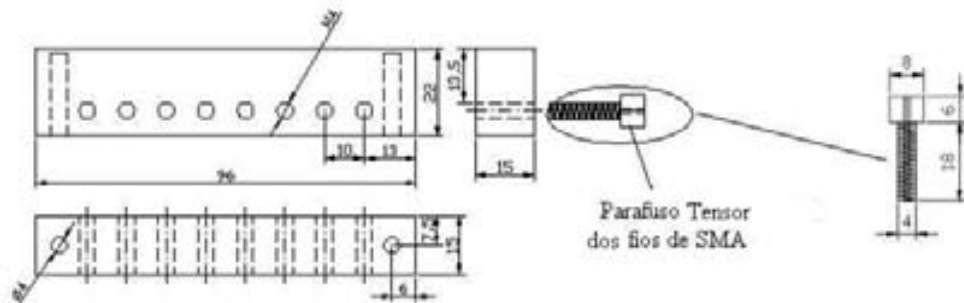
Detalhamento do suporte de fixação e parafuso de estiramento dos fios de SMA, dimensões em mm.
